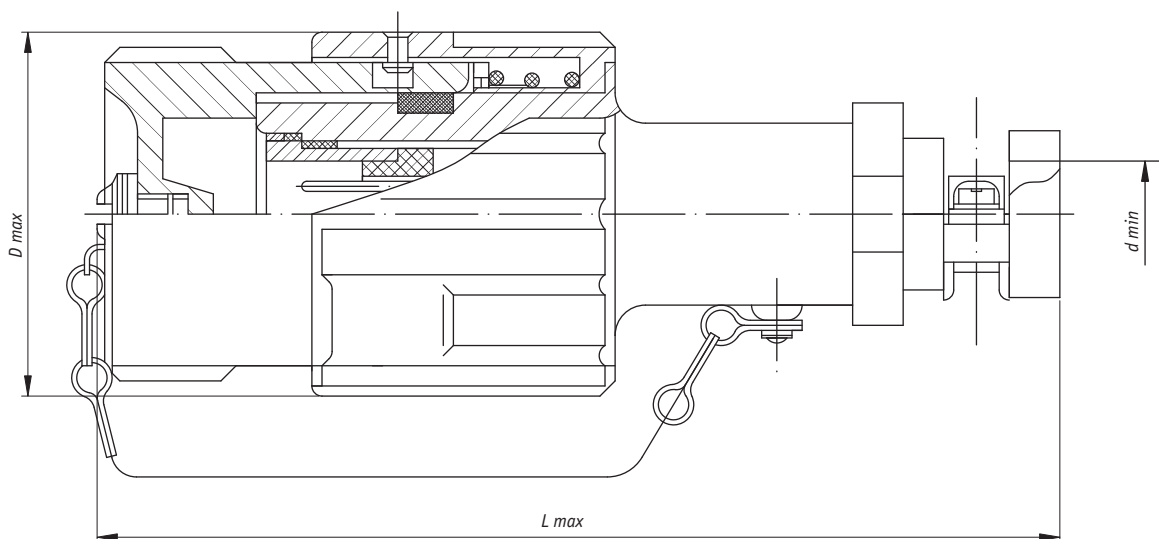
Вилка (розетка) кабельная в прямом корпусе
